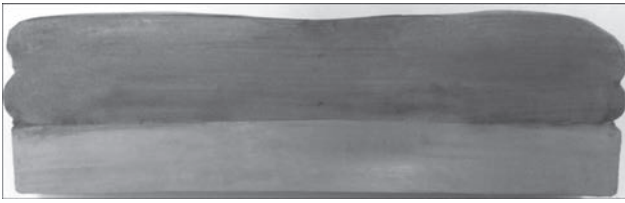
Макрошлиф биметаллической заготовки эксперимента 45М
